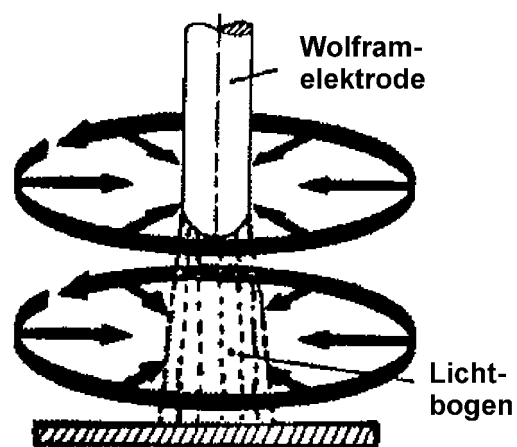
Magnetische Einschnürung des Lichtbogens bei hoher Schweißstromstärke
